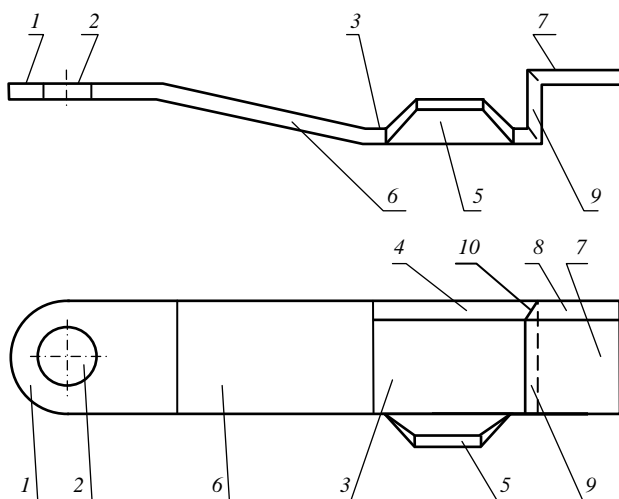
Изогнутый нож косилки-измельчителя: 1 – внутренний участок пластины; 2 – отверстие для крепления; 3 – периферийный участок пластины; 4 – боковая режущая кромка; 5 – подъемная пластинка; 6 – средний наклонный участок пластины; 7 – выступающая горизонтальная часть; 8 – боковая режущая кромка выступающей части; 9 – вертикальная часть; 10 – режущая кромка
